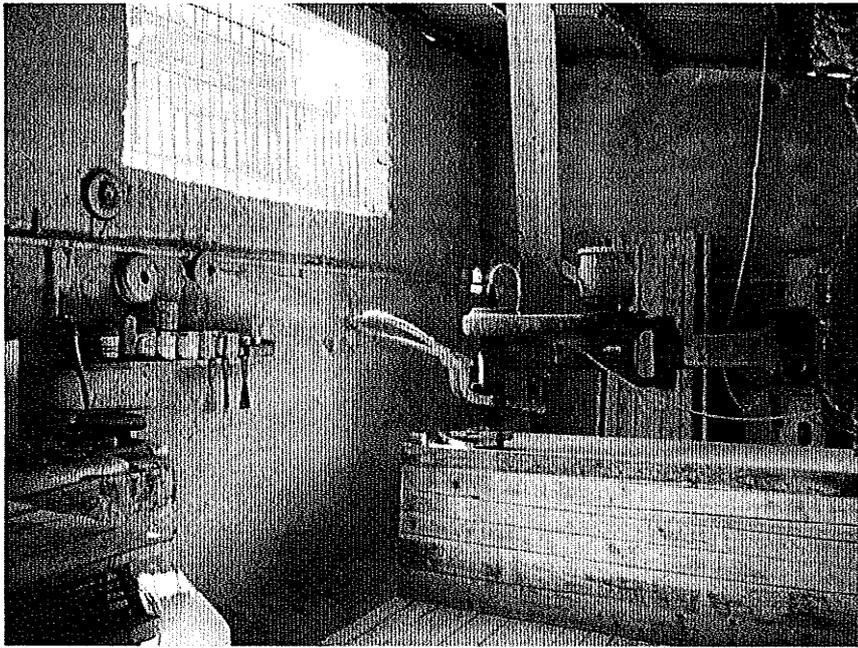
Particolare interno fabbricato A – Zona Lavorazione
